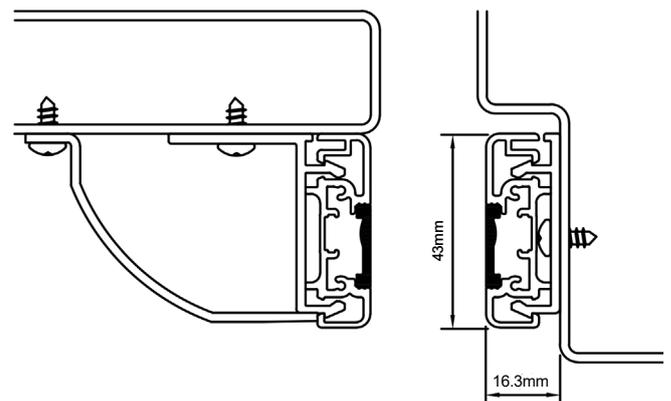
Perfil de 43 mm montado para apertura lateral con un soporte en «L» con protección para los dedos y soporte de poste de cierre
